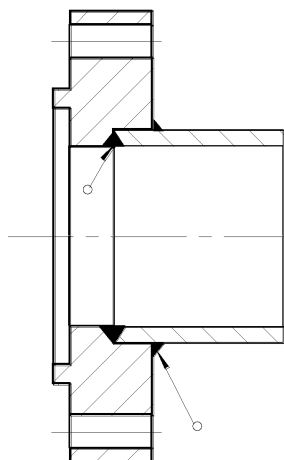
а – Конструкции фланцев стальных плоских приварных с соединительным выступом (гладкой уплотнительной поверхностью)
